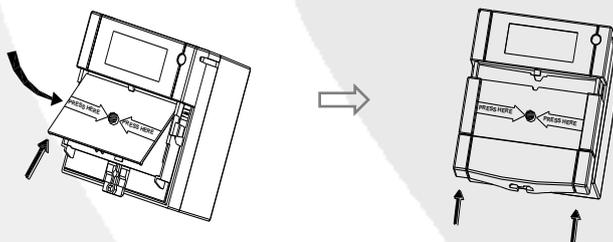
Recoloque o acrílico de operação e a parte frontal
